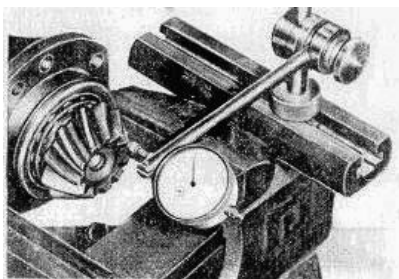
Проверка правильности регулировки осевого зазора в подшипниках ведущей шестерни главной передачи.
